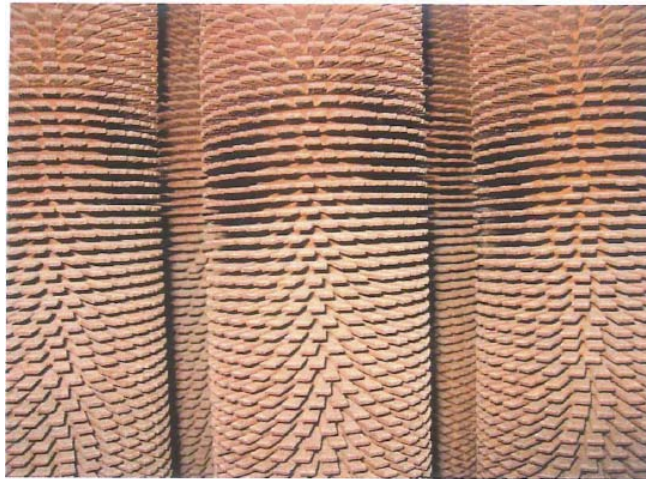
Tubos de aleta helicoidal, segmentada. Fuente: [9]
